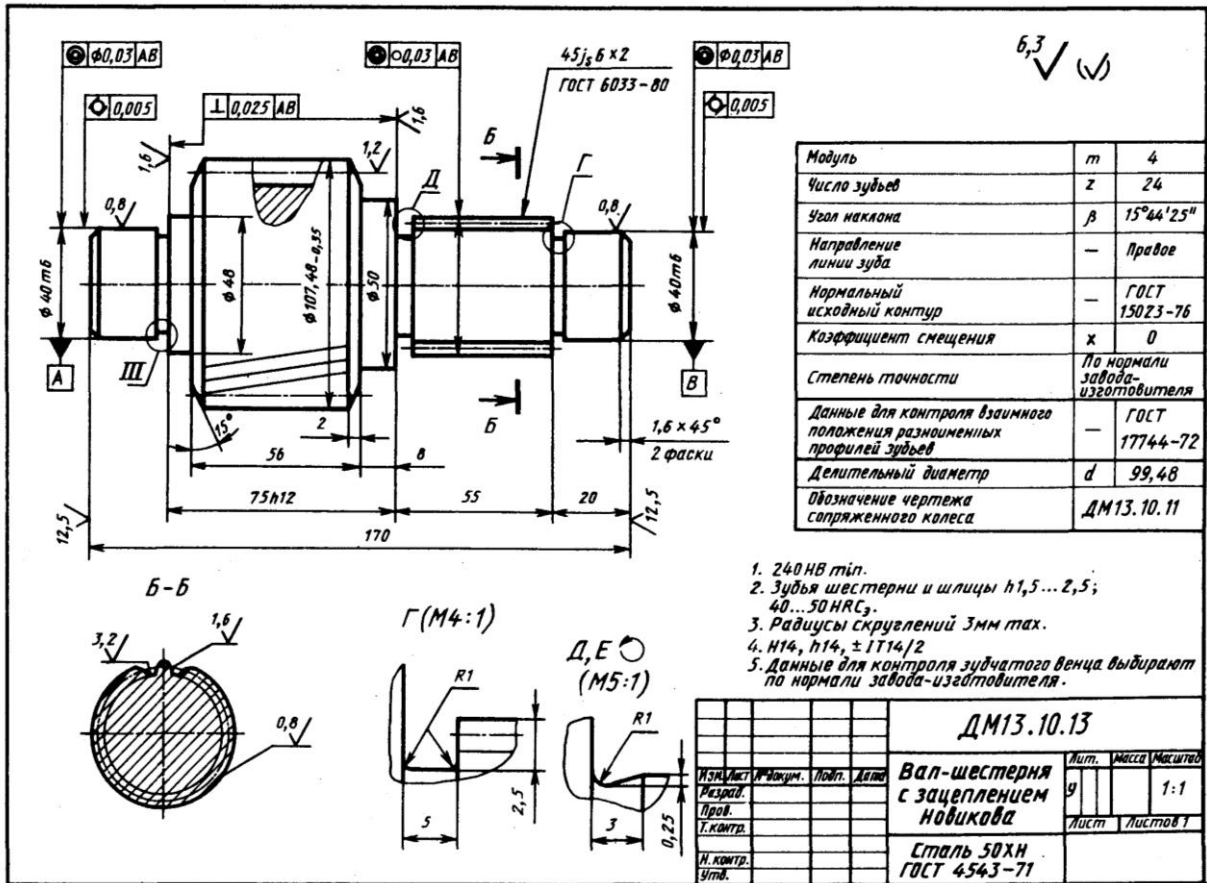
Креслення вала-шестерні із зацепленням Новікова
